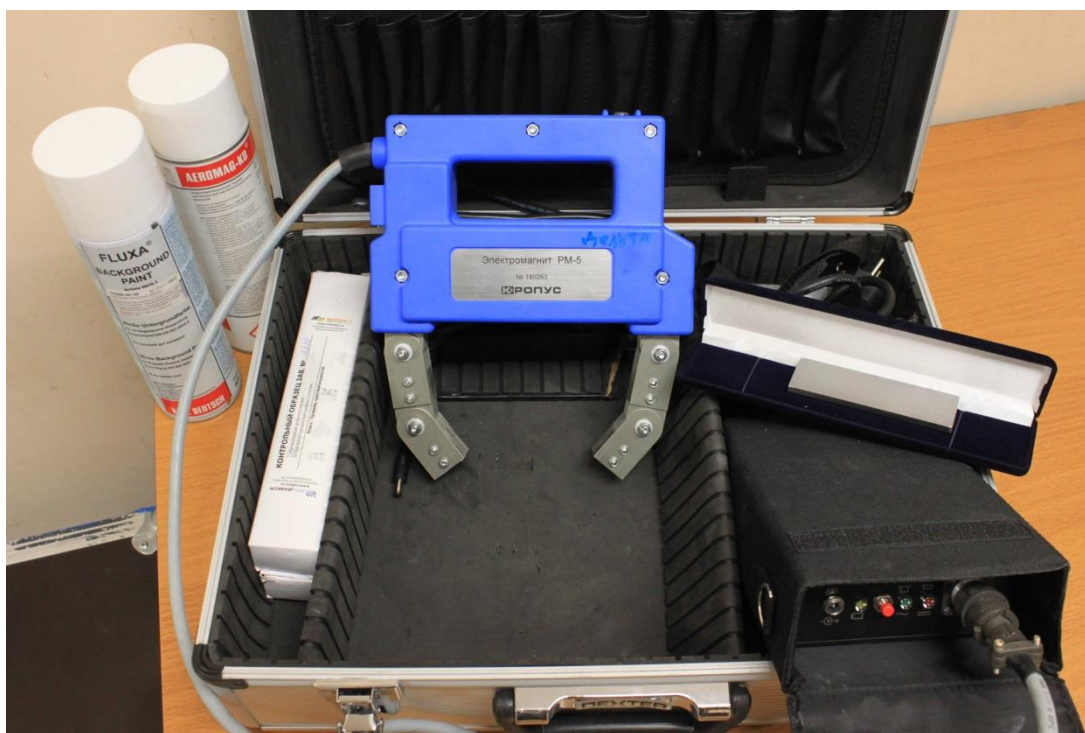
дефектоскоп для проведения магнитопорошкового контроля. РМ-5.
